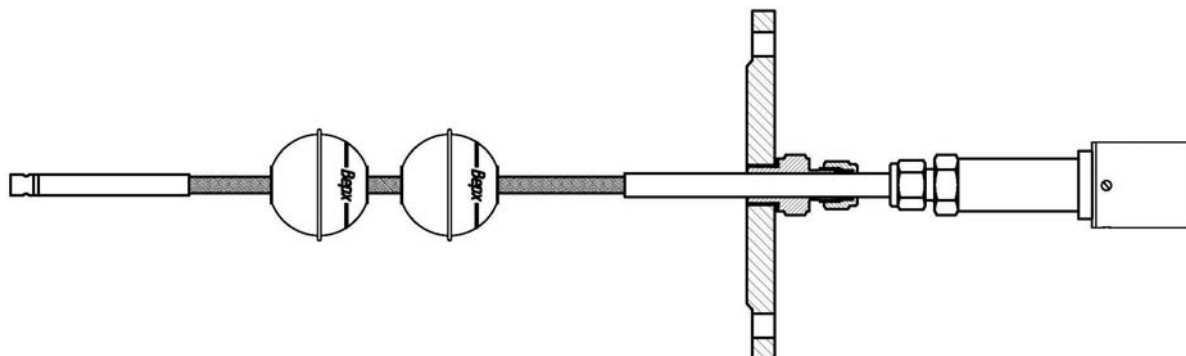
Установка штуцера, прокладки и крышки фланца
